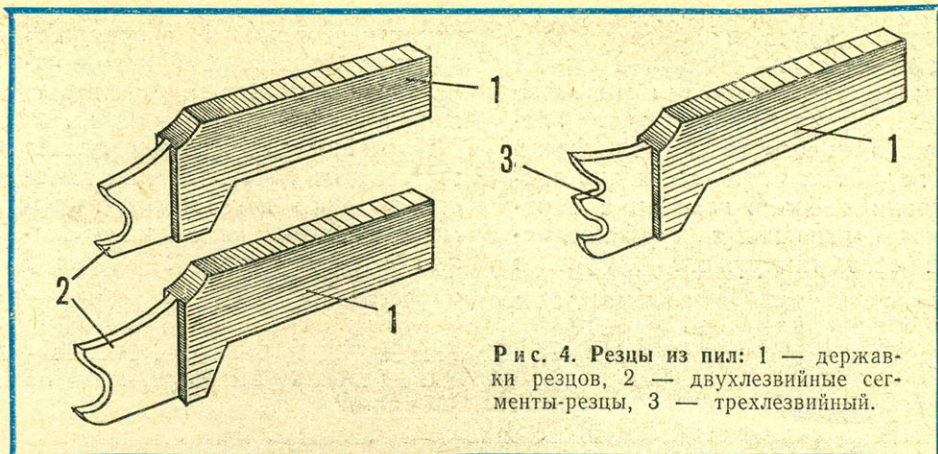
Резцы из пил: 1 — державки резцов, 2 — двухлезвийные сегменты-резцы, 3 — трехлезвийный.
